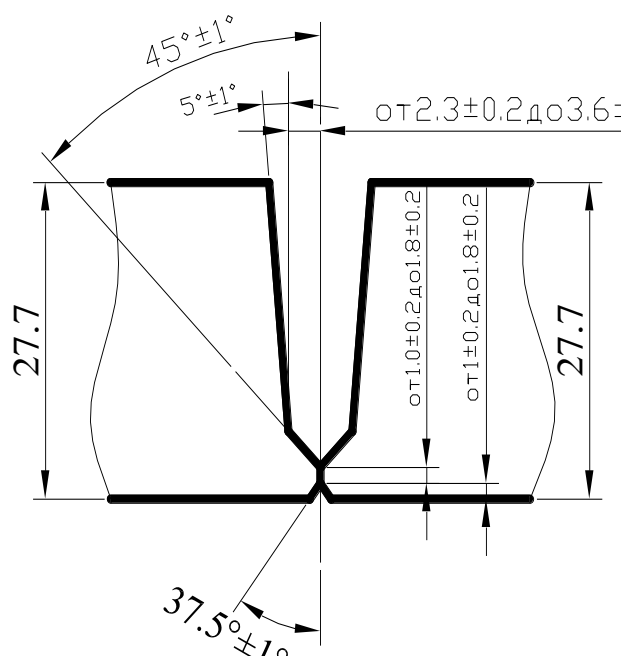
Подготовка кромок труб под сварку
